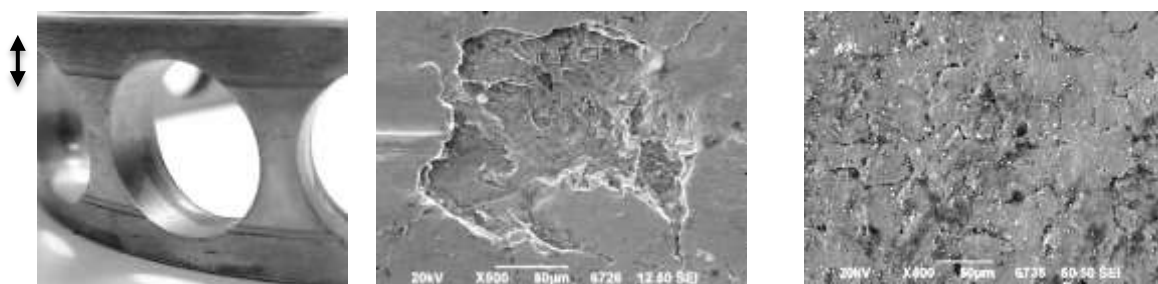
Состояние поверхности сепаратора подшипника № 2
